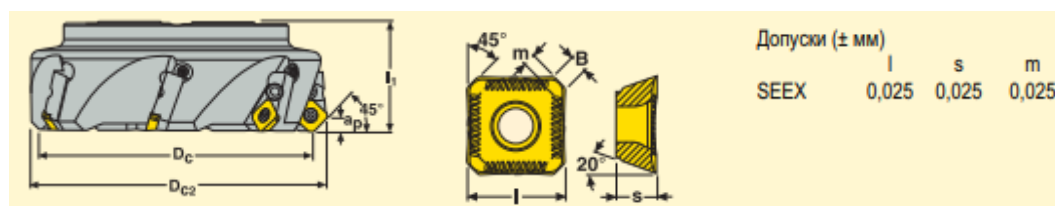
Торцева фреза для операції 010, R220.53-8315-09-18С, Розміри: $D_c=315$; $D_{c2}=325$; $l_1=80$; $a_p=4,5$; Кількість пластин: 18; швидкість: 3700 об/хв; матеріал пластини: МР3000; Пластина: SEEX 09Т3AFN-M05; матеріал: МР3000, Розміри: $B=1,5$; передній кут= 0° , $l=9,525$; $s=3,97$
